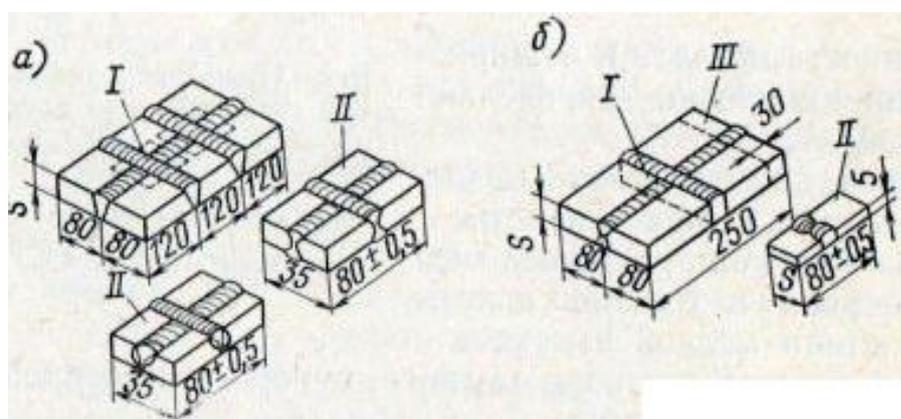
Образцы для испытания на межкристаллитную коррозию а - при толщине металла до 10 мм; б - при толщине металла более 10 мм; S - толщина металла; I - место вырезки образца; II - контрольная поверхность; III - отход
